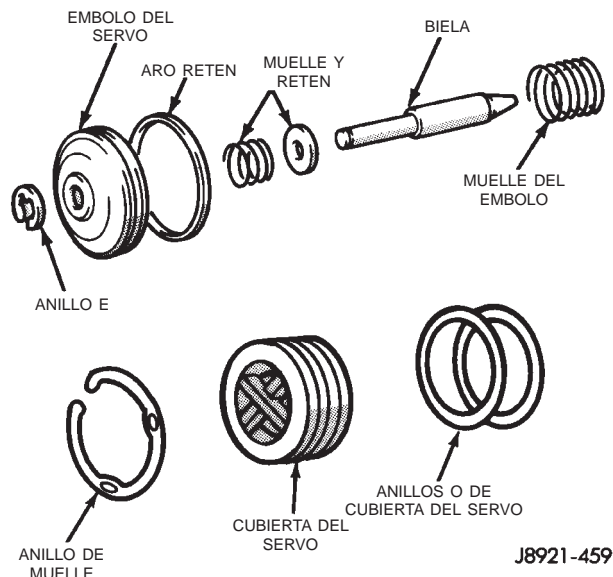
Componentes del émbolo de freno de rodadura libre en segunda
